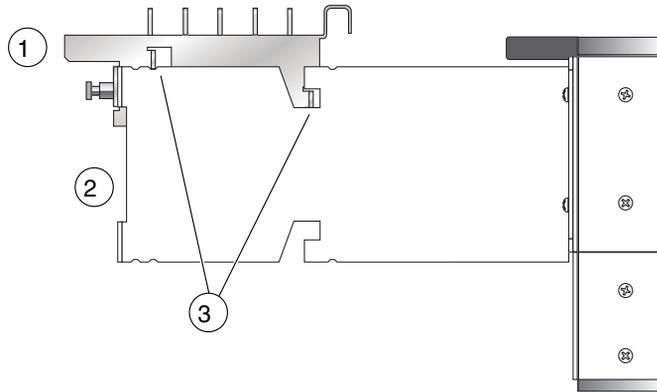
Vue latérale de la plaque de gestion des câbles et du support
